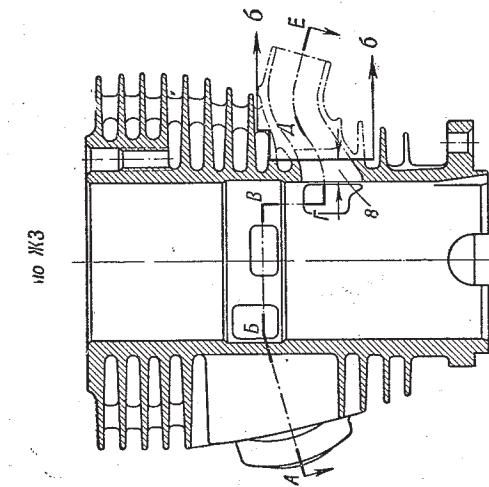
Подрезы цилиндра под съемный впускной патрубок:
